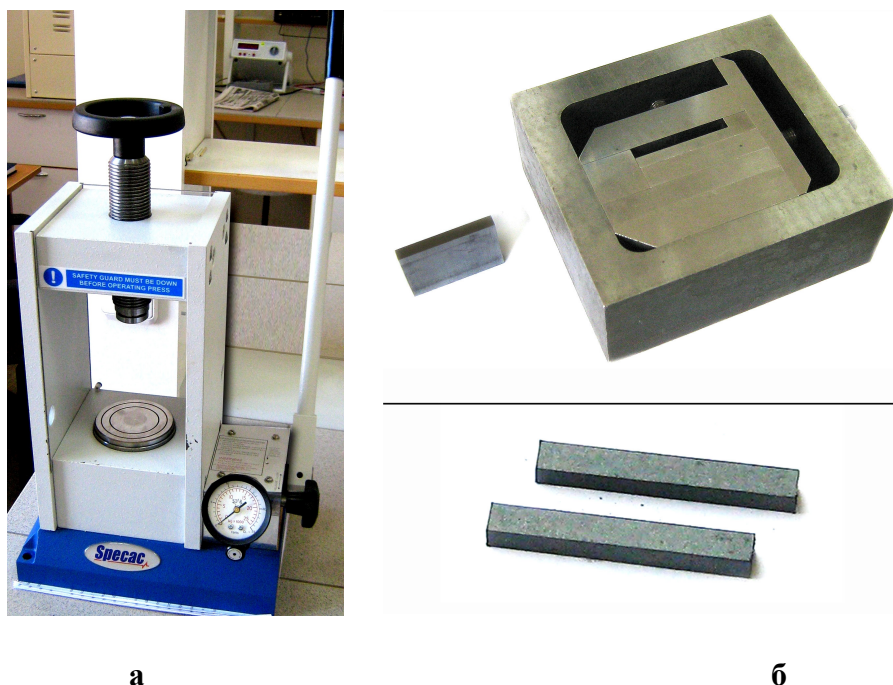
(а) - Гидравлический пресс, (б) – Пресс-форма (сверху), сырые балочки (снизу)
